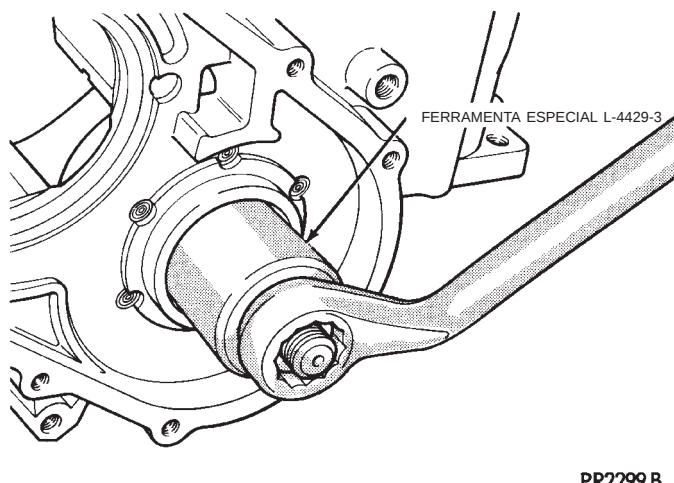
Instalação da Capa de rolamento da Engrenagem Circular Traseira com Dentes Interiores
